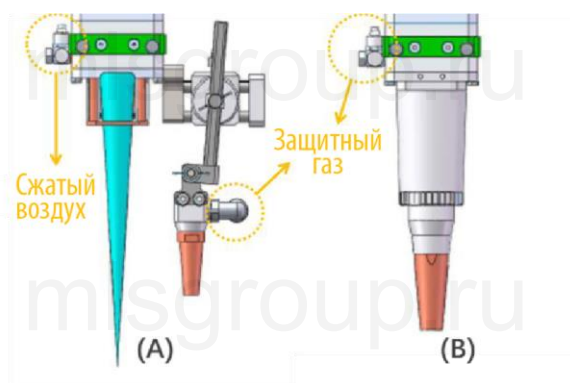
Подключение пневматической линии лазерной сварочной головки BW240
